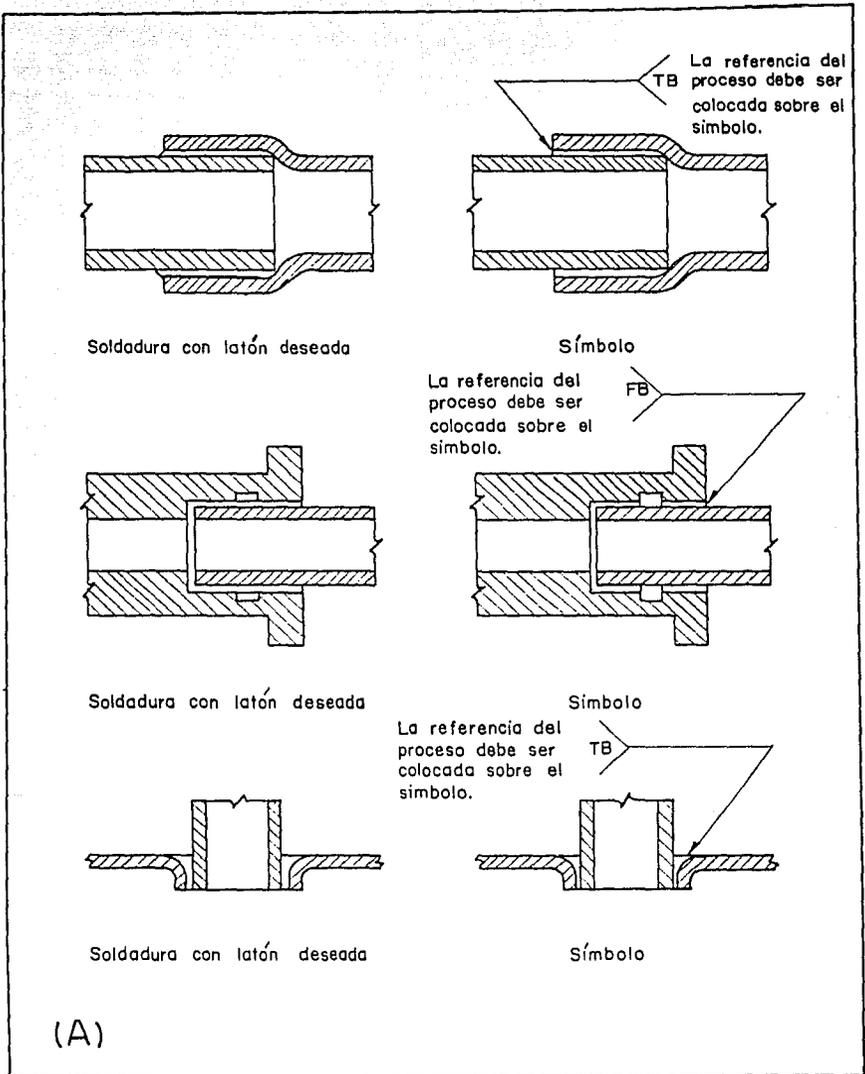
Aplicación de símbolos de soldadura con latón
